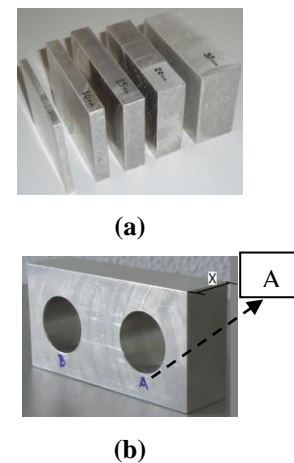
(a) Peças de alumínio fundido (b) Peça de alumínio laminado com X = 25,40 mm
